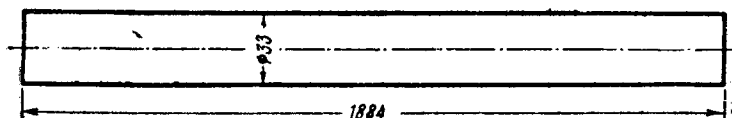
Заготовка для ствола винтовки обр. 1891/1930 гг.
